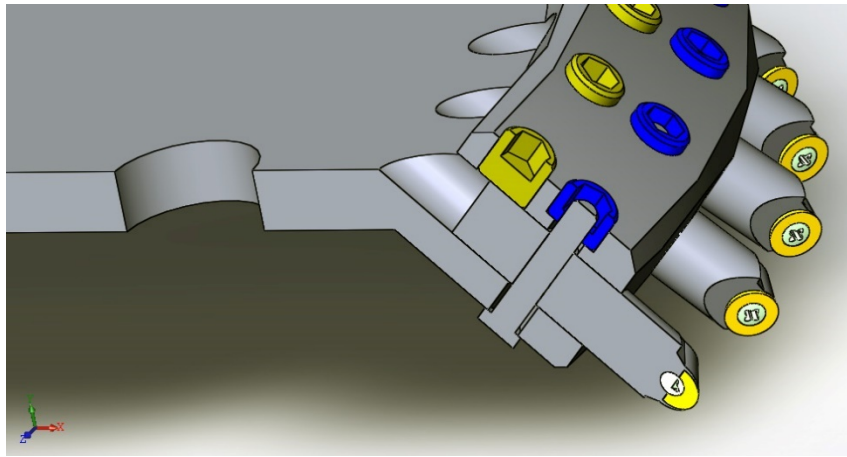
Вузол кріплення циліндричної різальної вставки в торцевій фрезі з додатковим стопорним гвинтом
